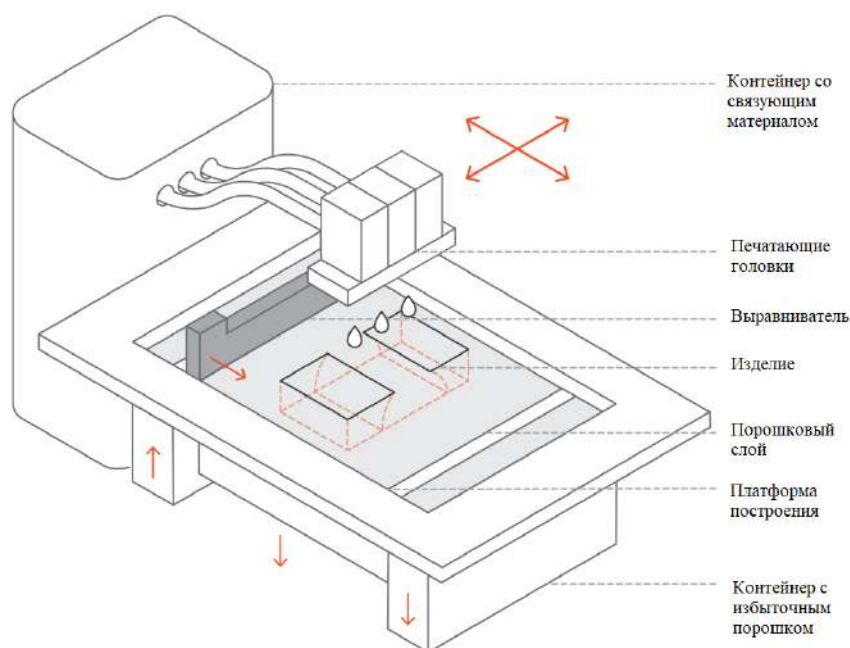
Схема работы металлического принтера струйной печати
